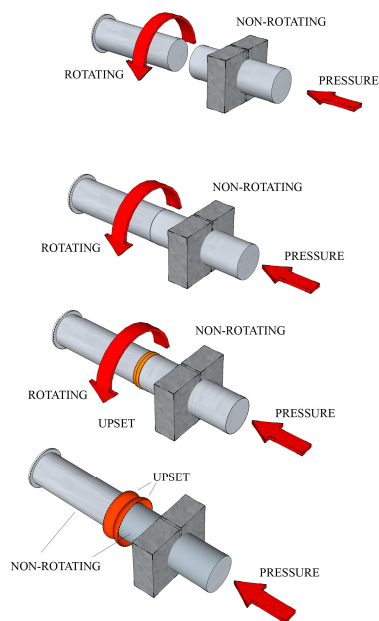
Rappresentazione schematica del processo “spin welding”
